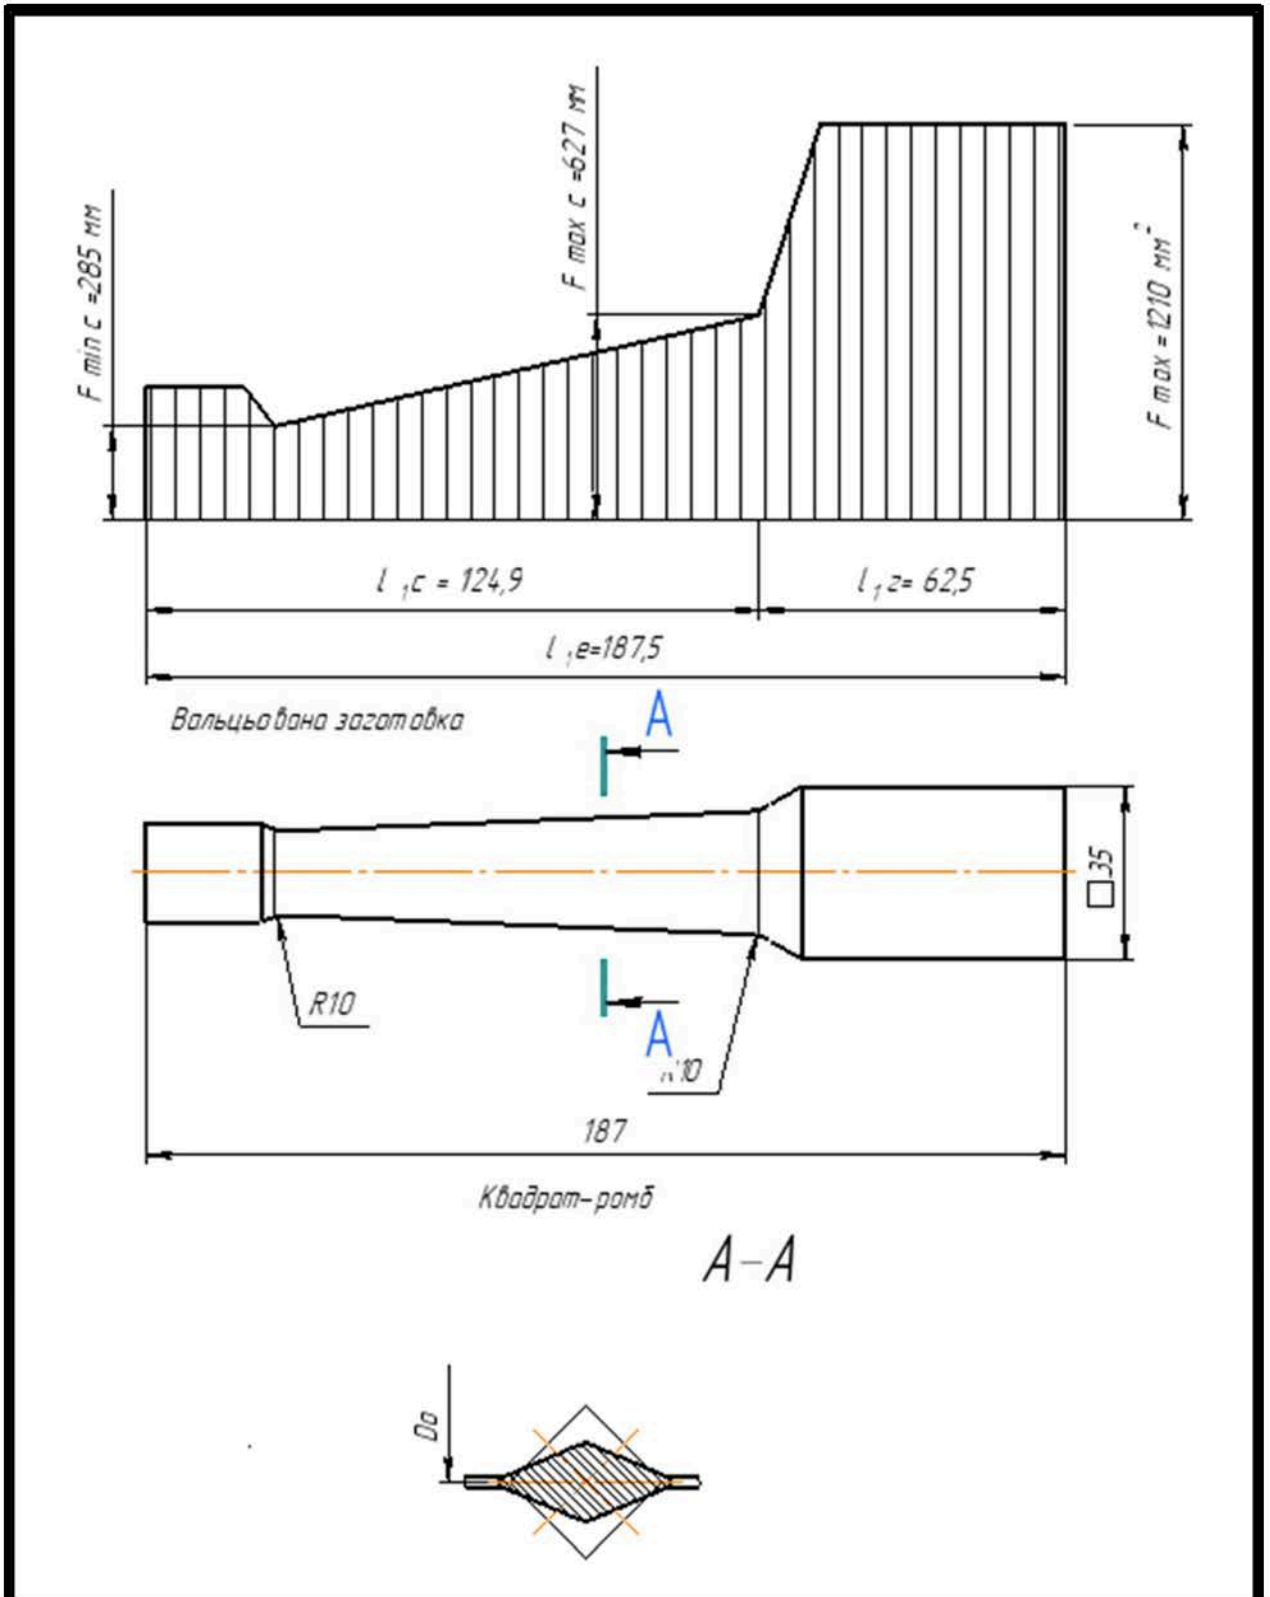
Епюра перерізів вальцьованої заготовки
